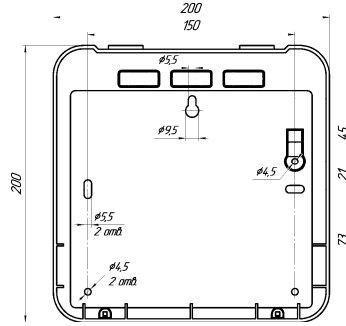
Розмітка отворів для кріплення корпусу модуля
